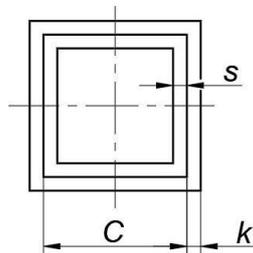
Форма расчетного сечения сварного шва.
